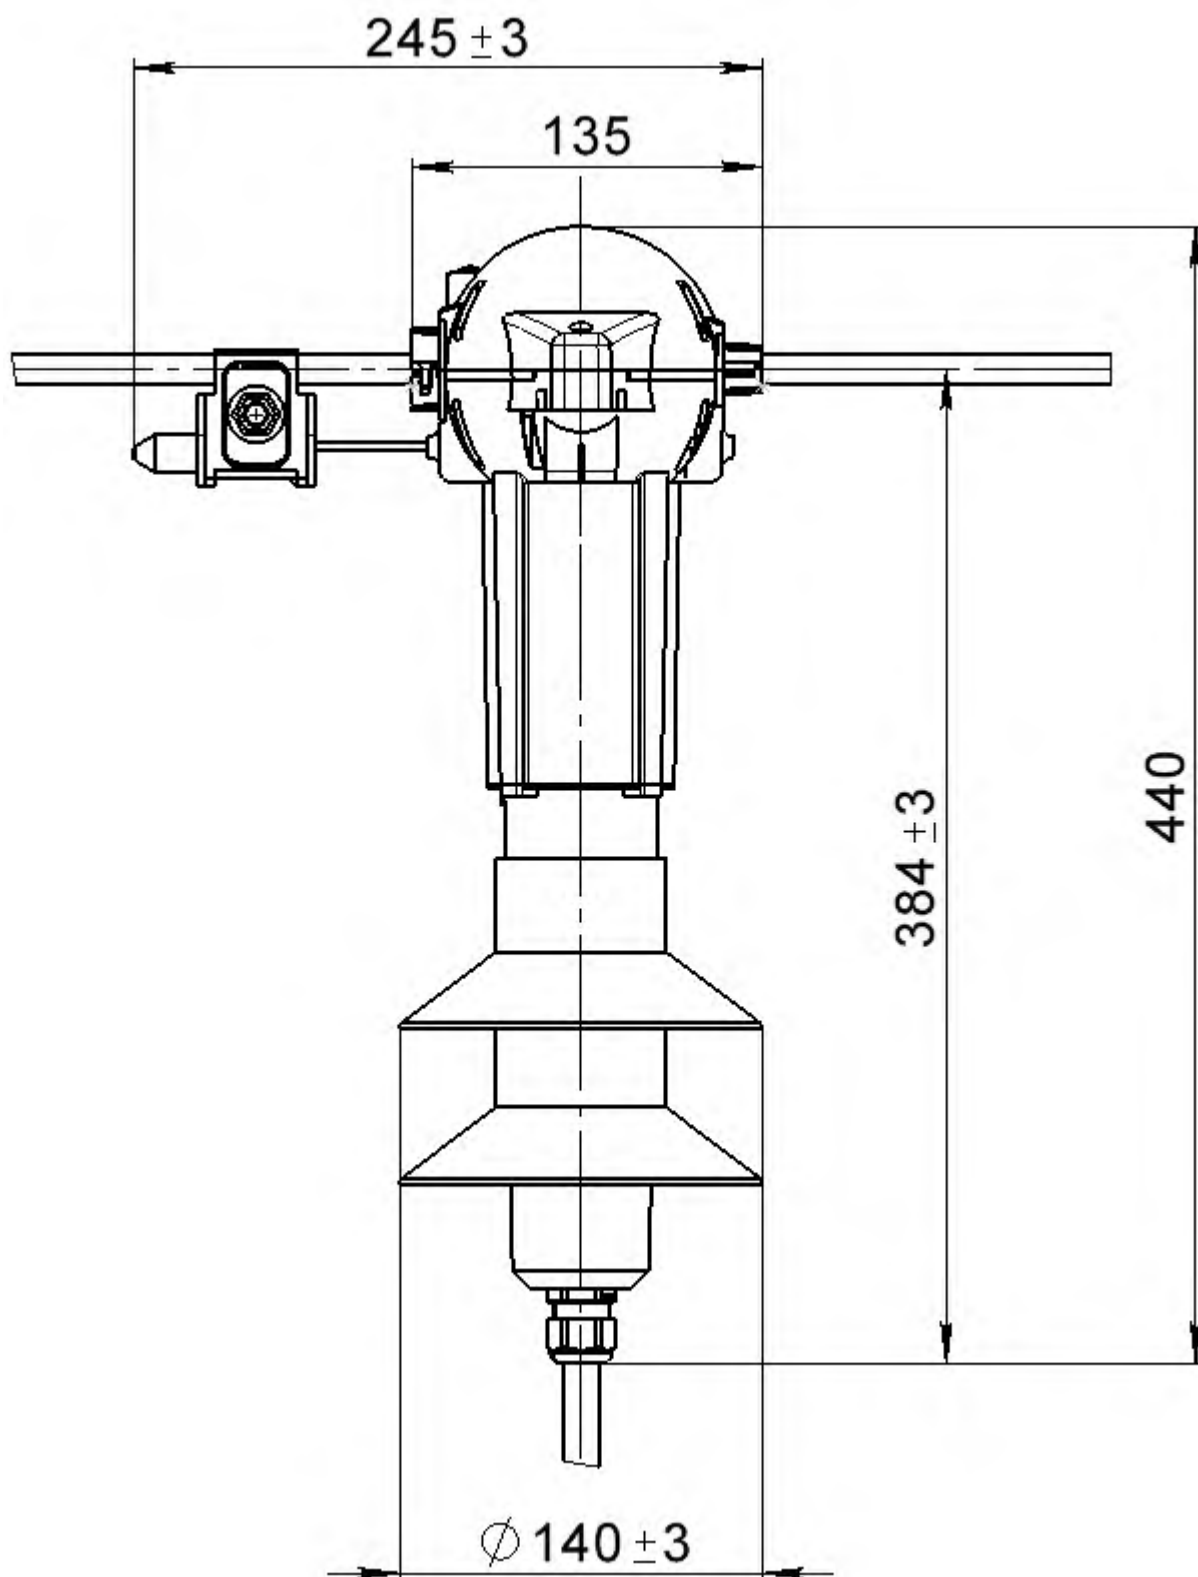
Габаритные и установочные размеры БИ1, БИ2
